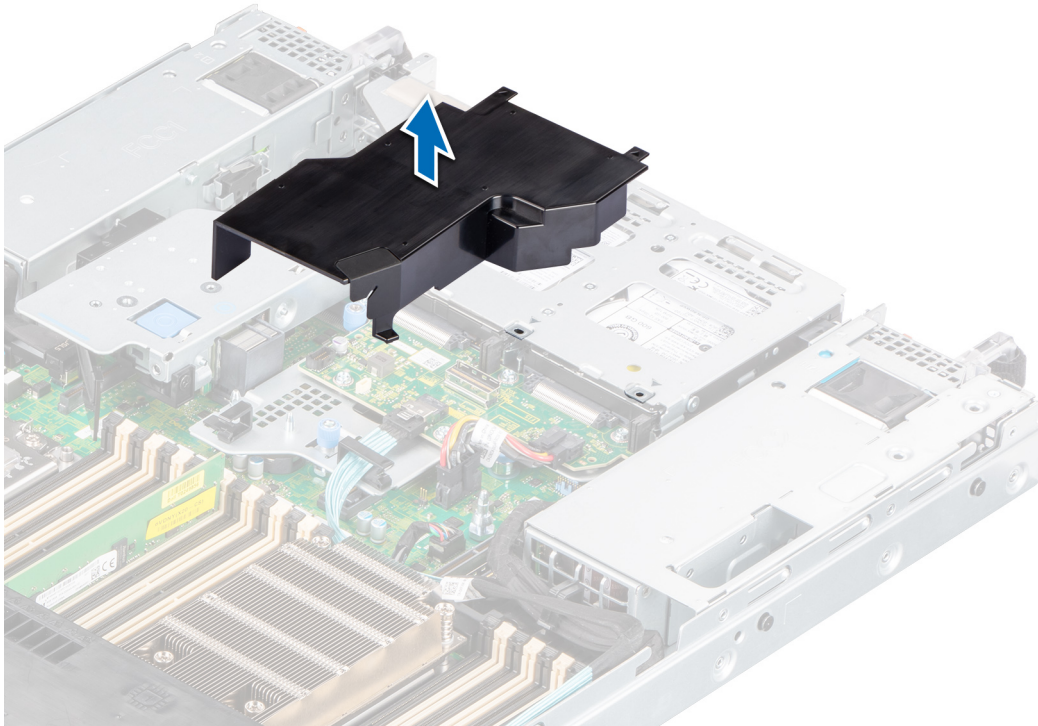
Entfernen des Kühlgehäuses aus dem hinteren Laufwerksmodul
